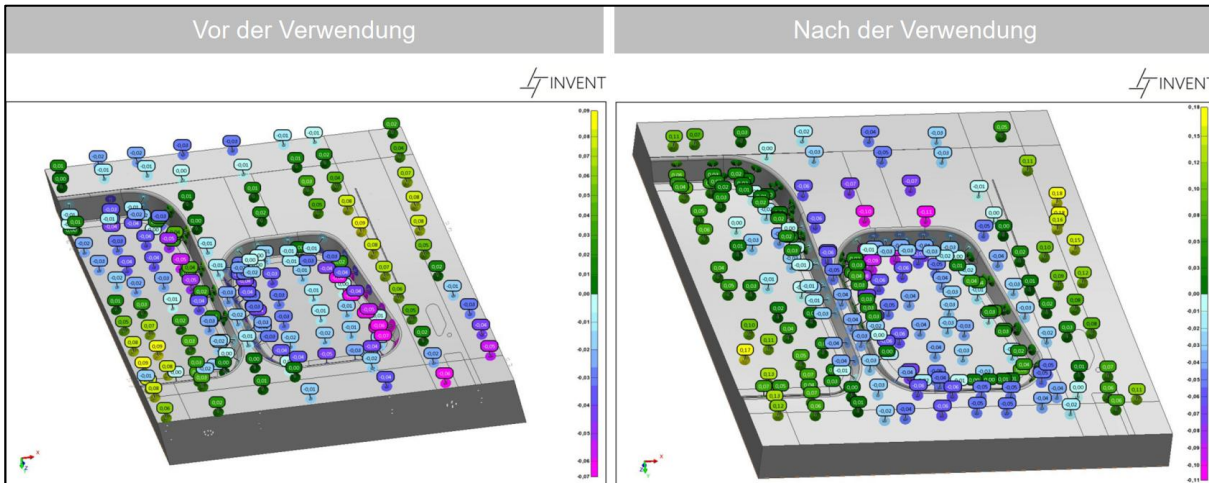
Abweichungen der Werkzeugoberfläche vom CAD-Modell für das Werkzeug aus dem Material PC-C. Die Abweichungen sind in mm angegeben.
